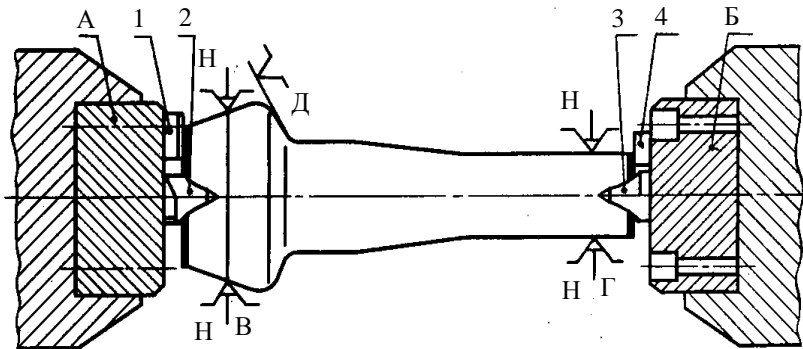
Схема обробки торців деталі на центрально-підрізному напівавтоматі АЛ:
